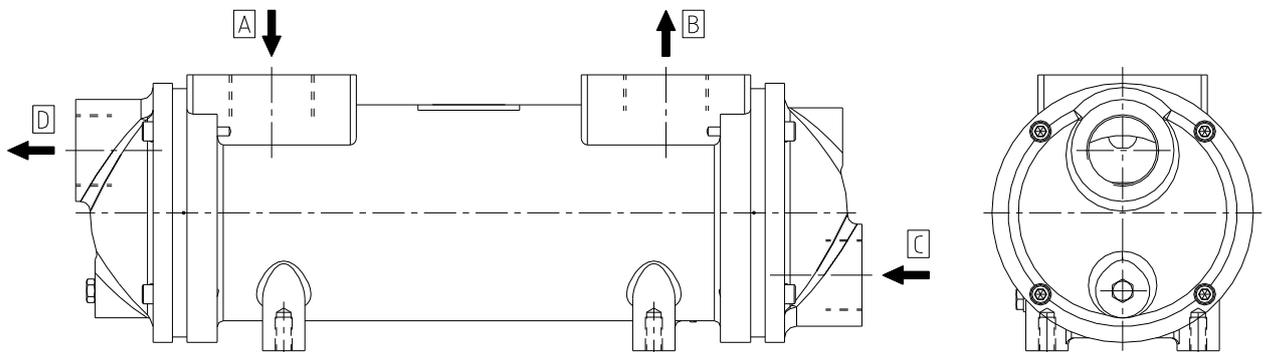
Öl-/Wasserkühler Ausf. TAK/T Serie 27 und 28
